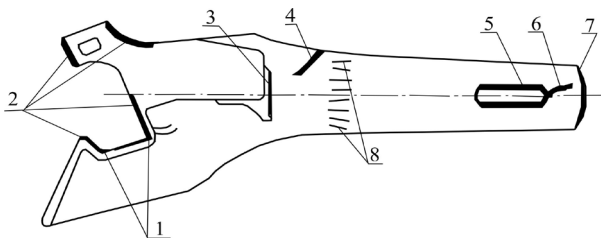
Места повреждений и износов корпуса автосцепки
